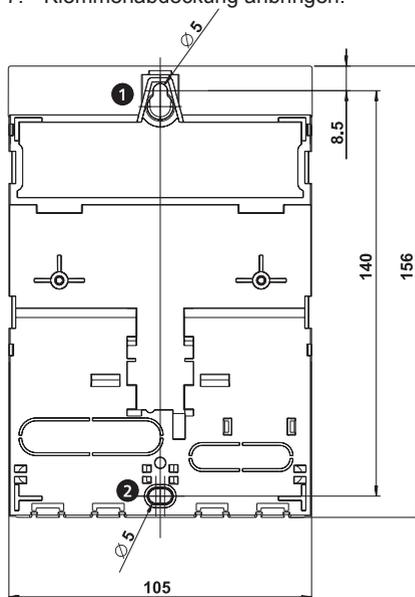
Rückseite des Reglers mit Montageöffnungen oben ❶ und unten ❷
